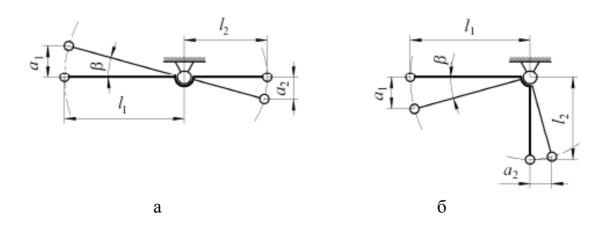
Схема перемещения рычагов при неточном изготовлении длины их плеч: а - прямых; б – угловых
